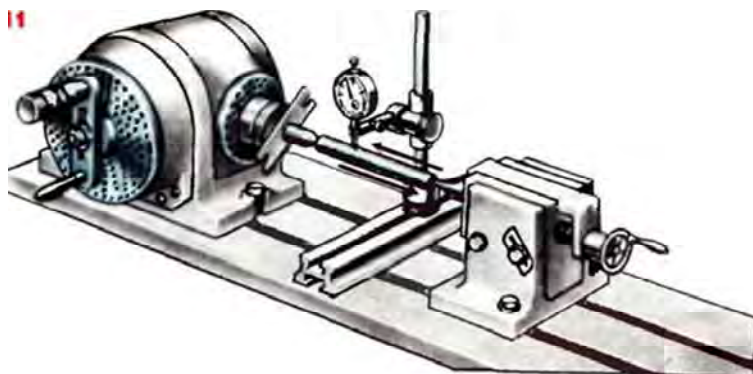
Проверка совпадения центров УДГ и задней бабки
